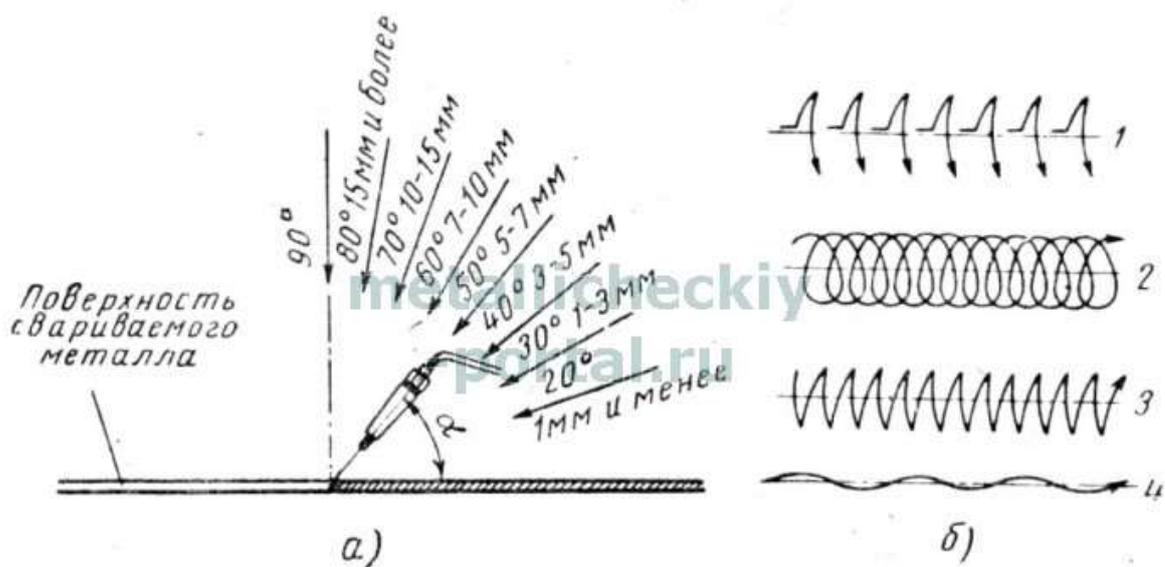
Углы наклона (а) и способы перемещения (б) мундштука при газовой сварке
